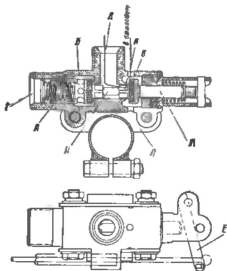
Пусковой клапан (положение клапанов при выпуске воздуха из цилиндра в атмосферу).
